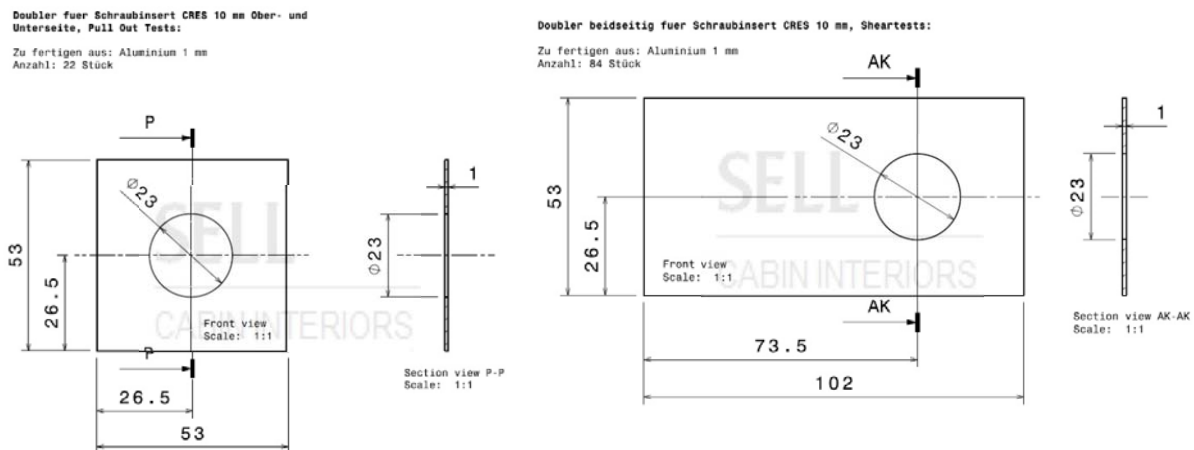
Unterschiedliche Dimensionen der Doubler (lokale Deckschichtverstärkungen) für die Pull-out- (links) und Shear-Testkörper (rechts) der Schraubinsert im Sandwichtyp 618 HC.
